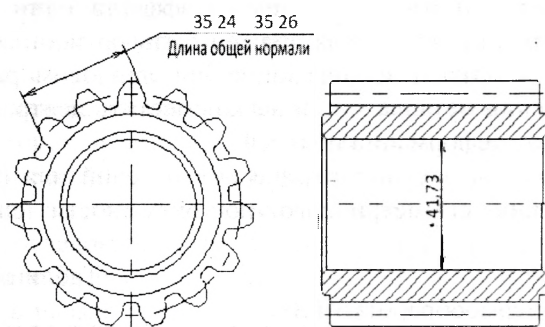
Общий вид детали 5336-2405035 — сателлит
